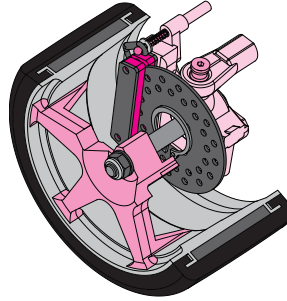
Exemple de liaison plan sur plan : les plaquettes de frein d'une voiture sur le disque lié à la roue.
